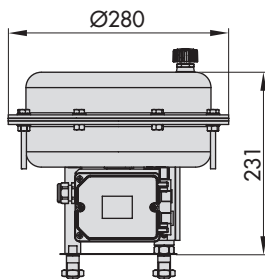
Desenho dimensional da versão de 350 cm²
